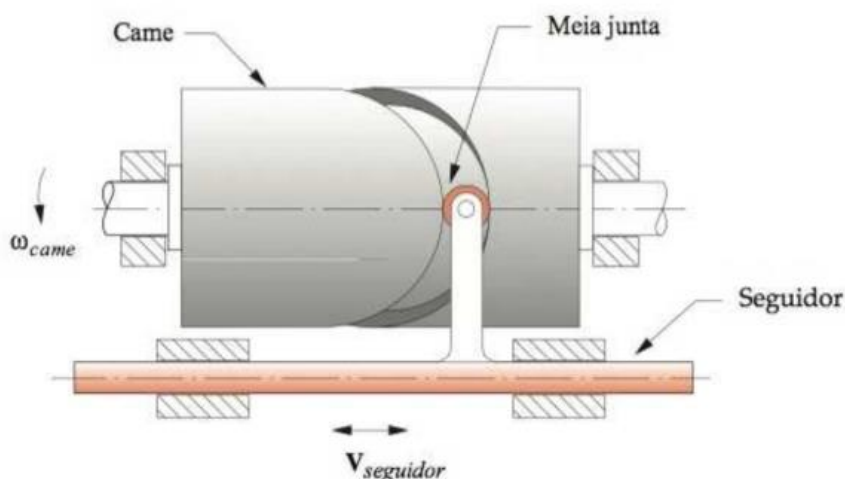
Came axial, de rolete ou tambor unido por forma, seguidor de translação.
